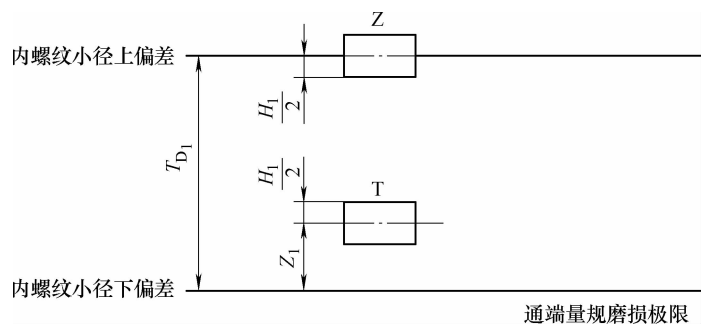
检验工件内螺纹小径用的光滑极限量规尺寸公差带图
